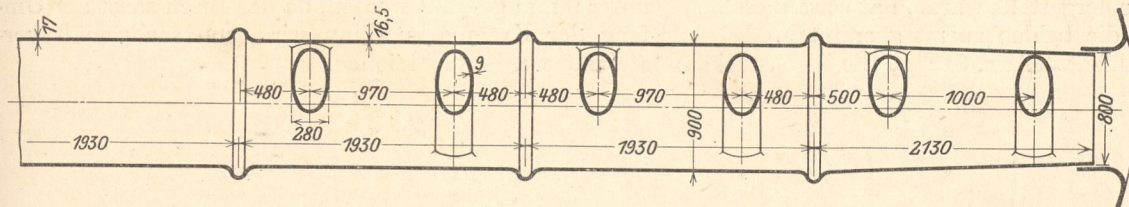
Flammrohr mit Pommé-Wellen und eingeschweißten Quersiedern.
